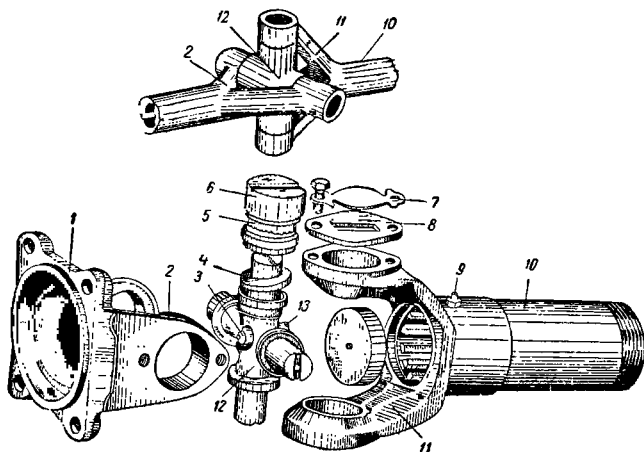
Схема и детали шарнирного сочленения автомобиля ЗИЛ-150.
